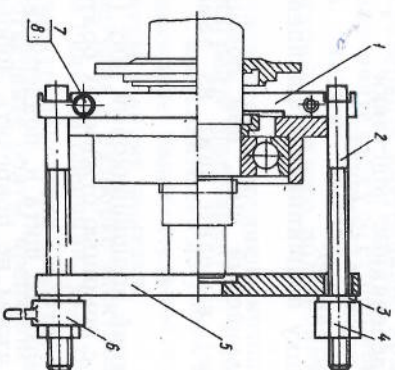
Съем шарикового подшипника электродвигателя исполнения IM3011:
